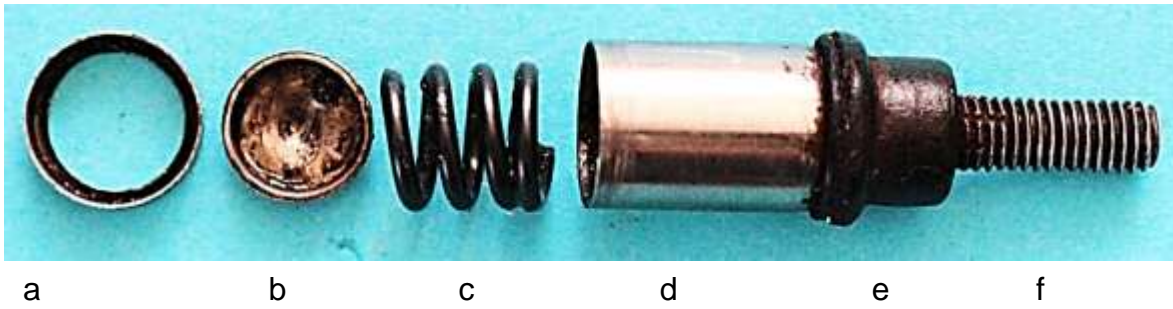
Einzelteile des Axiallagers: a) Sicherungsring, b) Kugelpfanne, c) Schraubenfeder für den Axialspielausgleich, d) Federzylinder, e) Isolierteil, f) Kabelanschlussbolzen
